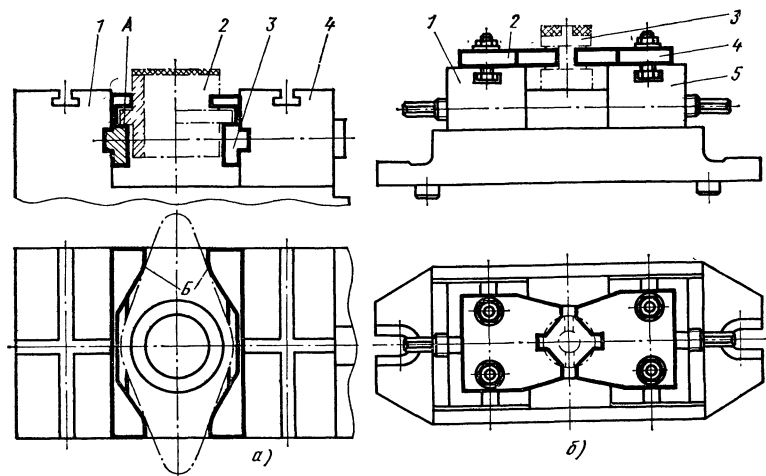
Наладки к универсальным наладочным тискам для закрепления деталей типа фланцев
